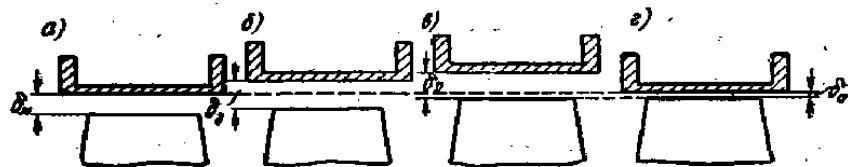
Радіальні зазори між корпусом і робочими лопатками турбіни:
